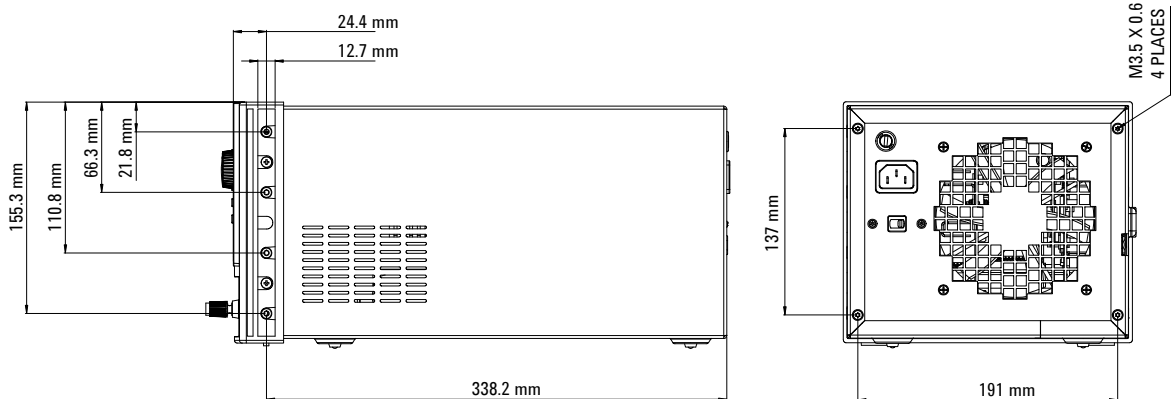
Dimensiones del montaje en bastidor Serie U8030A
